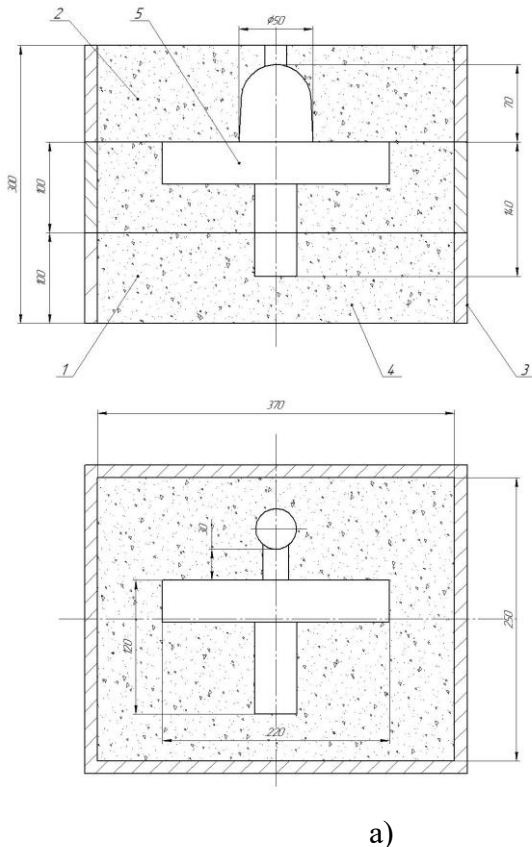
Базовий вузол конструкції станини металообробного верстата
